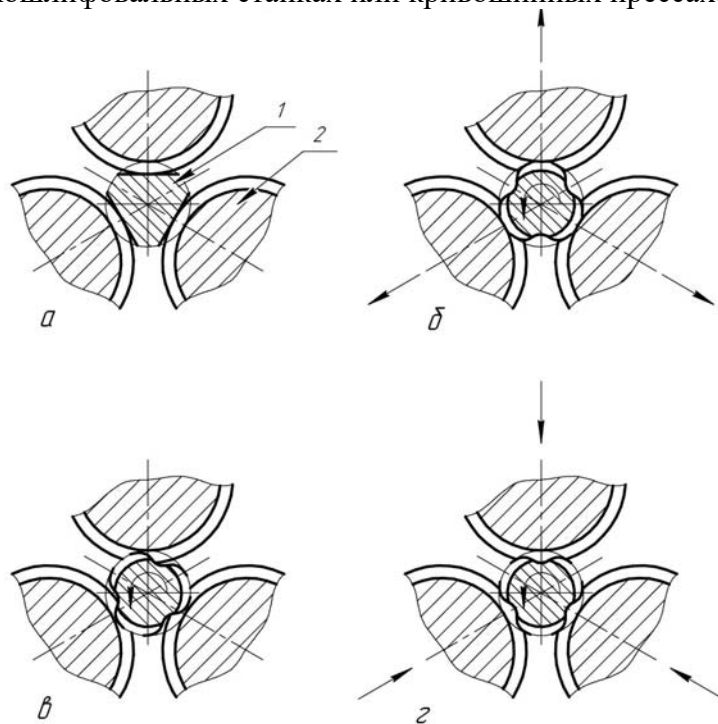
Схема способа (авт. свид. SU 1065069) образования затылованного резьбового профиля на рабочей части ПДМ: а – исходное состояние заготовки ПДМ и резбонакатных роликов; б – вращение заготовки и согласованное продольное перемещение резбонакатной головки к вершинам граней; в – продолжение указанных перемещений резбонакатной головки с обеспечением затылования профиля; г – продолжение указанных перемещений резбонакатной головки ко впадинам граней с обеспечением формирования смазочных канавок
